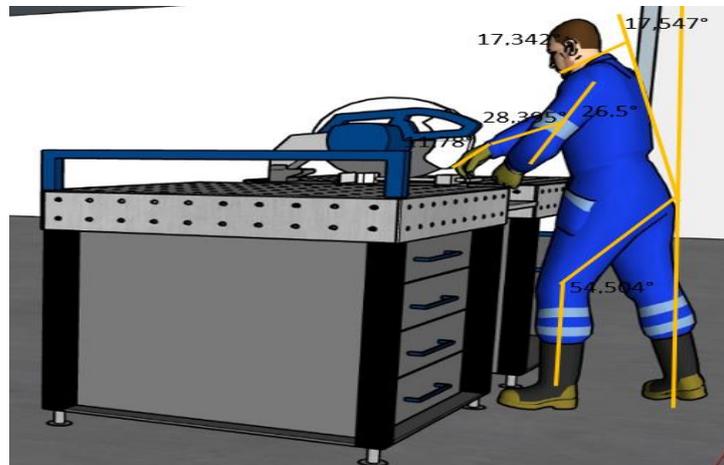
Skor REBA Welder 1 Setelah Perbaikan
